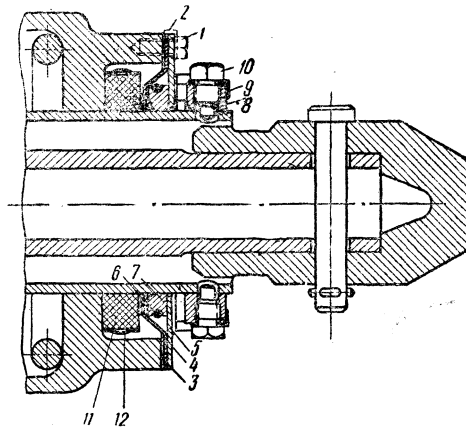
Сальник штока (трубы) тормозного цилиндра
